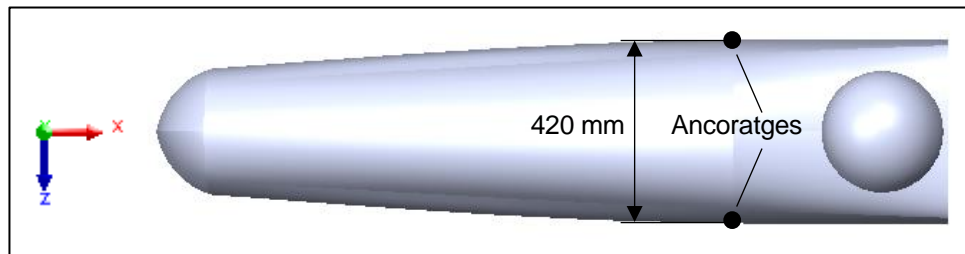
Vista en planta amb les dimensions de la part davantera de la cadira.
